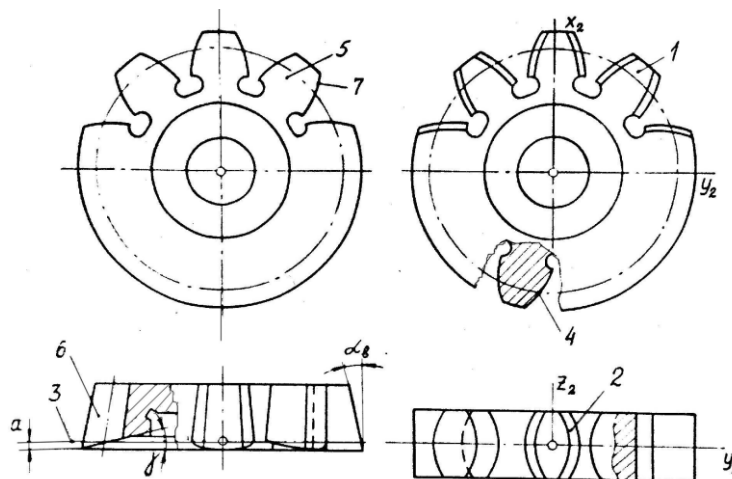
Производящее цилиндрическое колесо и обкаточный лезвийный инструмент на его основе
